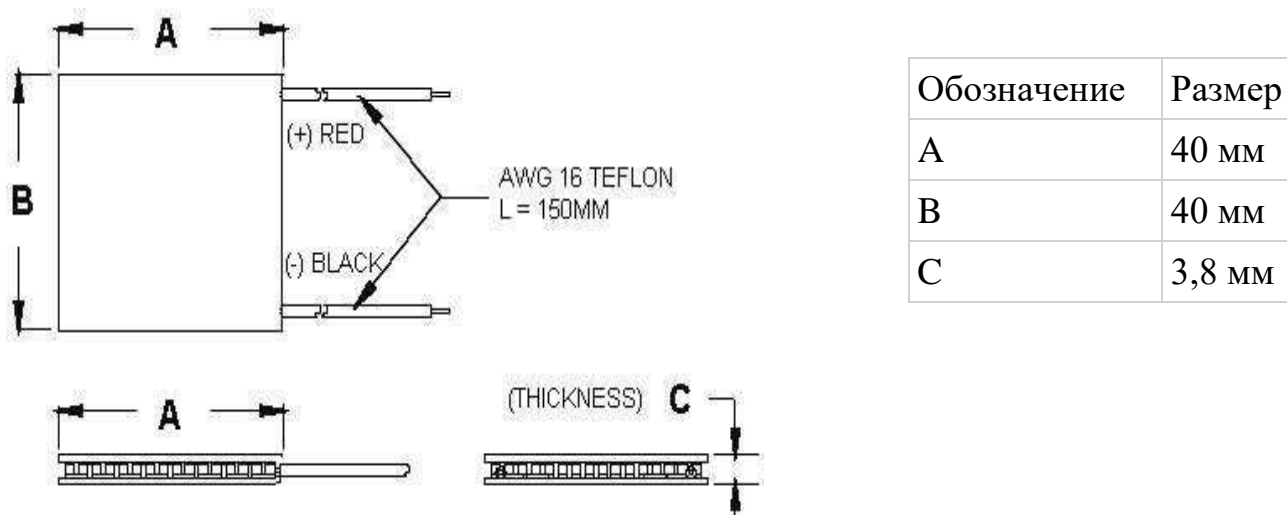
Габаритный чертеж модуля TEC1-12706.
